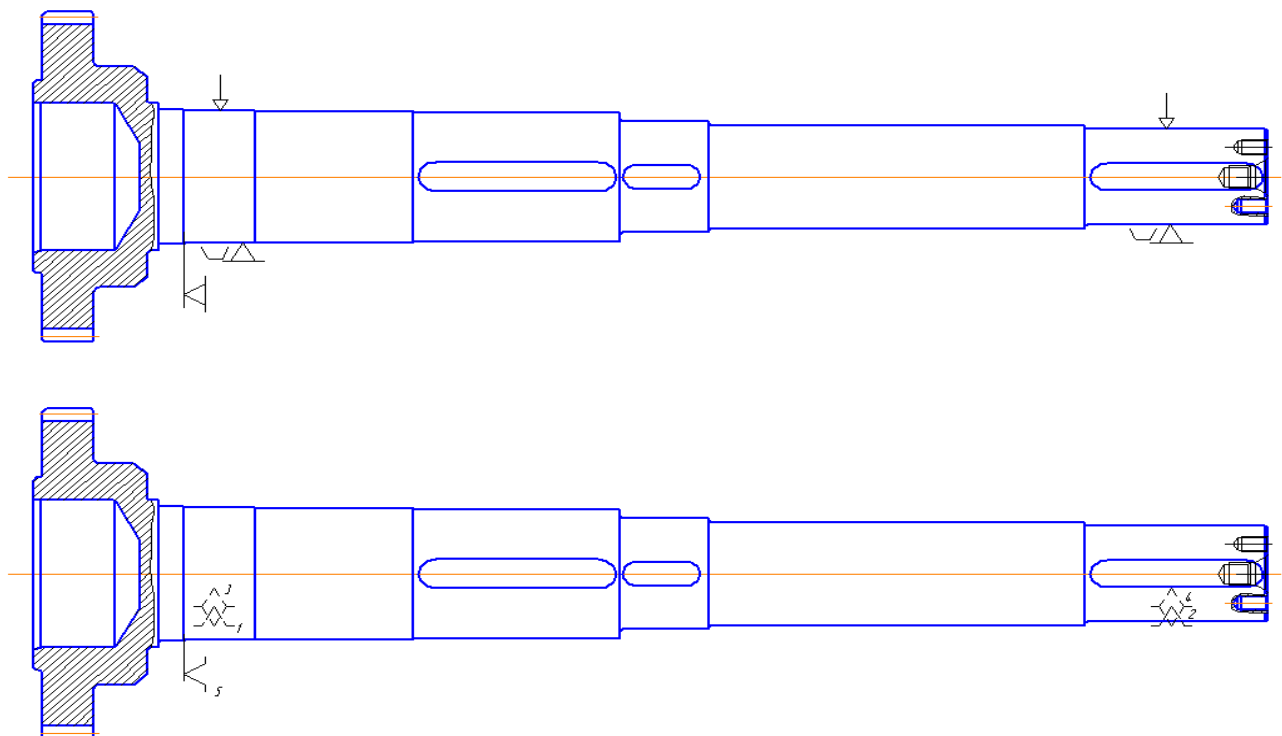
Умовна та теоретична схема базування при фрезерній та свердильній операціях
